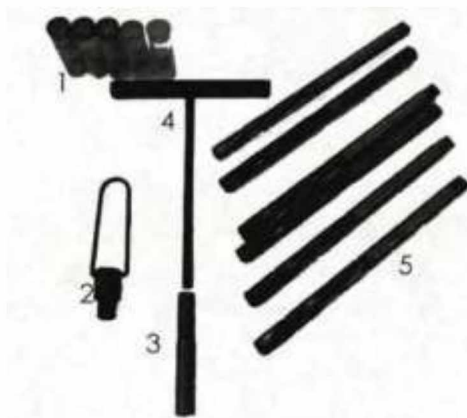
Індикаторний пристрій для перевірки биття сідла клапана
